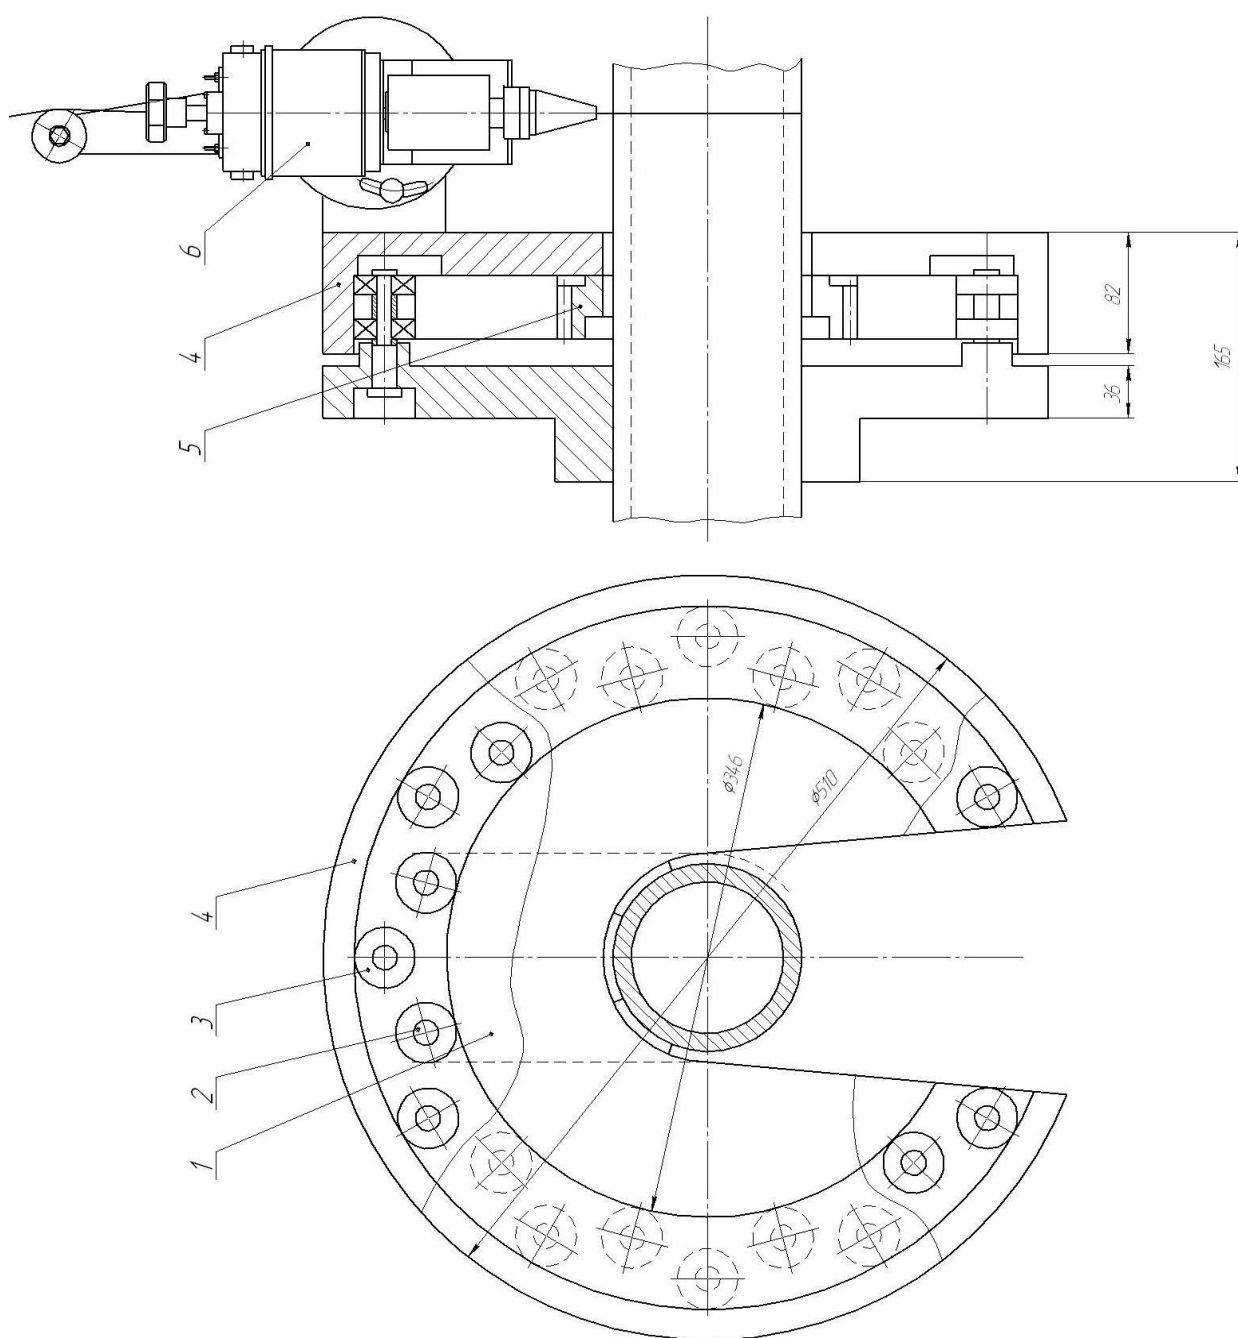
Предлагаемое устройство для автоматизации сварки труб
